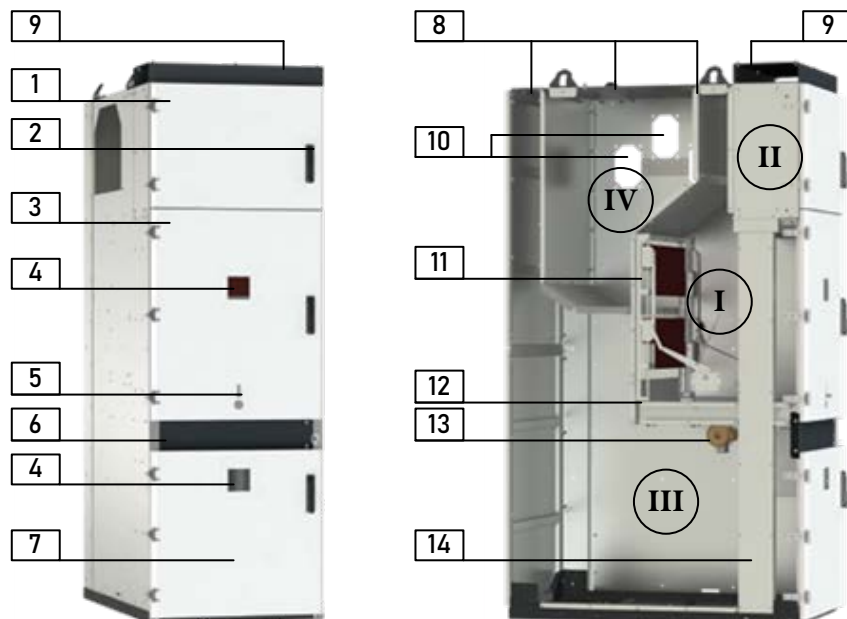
Конструкция корпуса ячейки ТРАКТ
